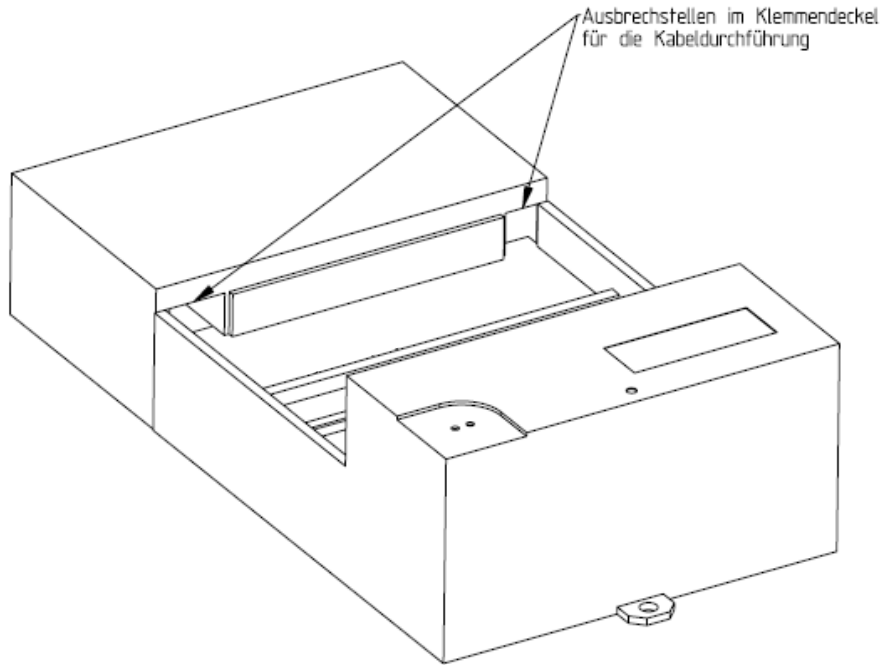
Ausbrechflächen im Klemmendeckel für die Kabeldurchführungen
